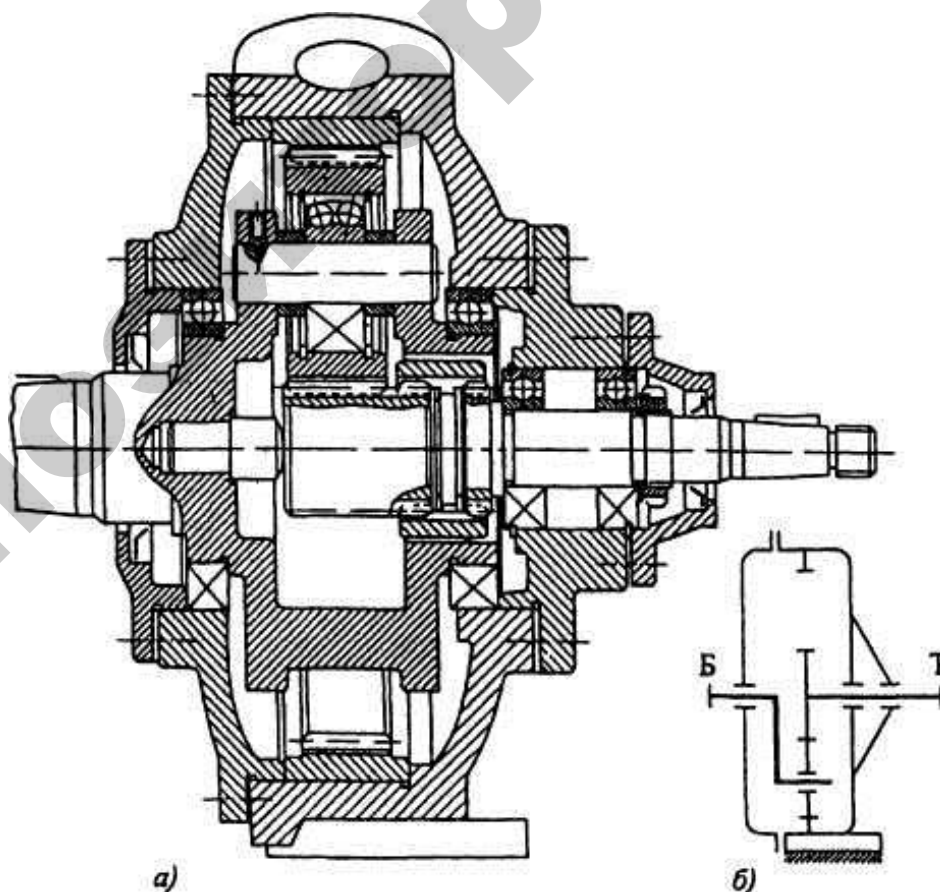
Планетарный редуктор: *а* — конструкция; *б* — кинематическая схема.
